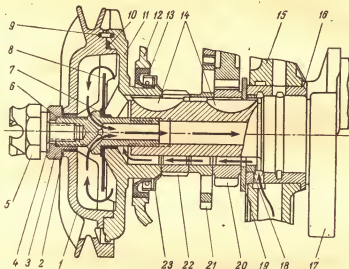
Центробежный маслоочиститель и передний коренной подшипник коленчатого вала двигателя «Запорожец»:
